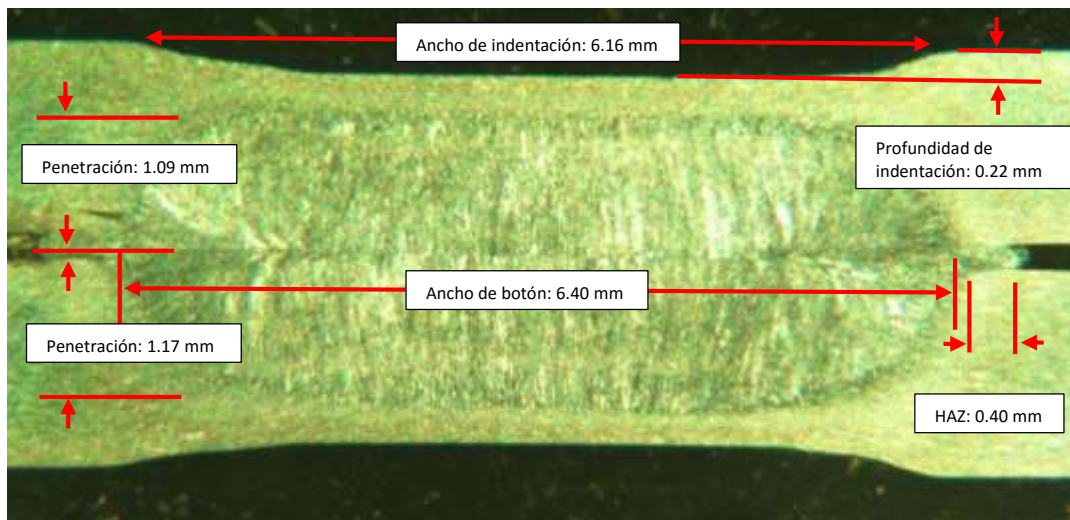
Mediciones realizadas en el botón de soldadura número 13.
